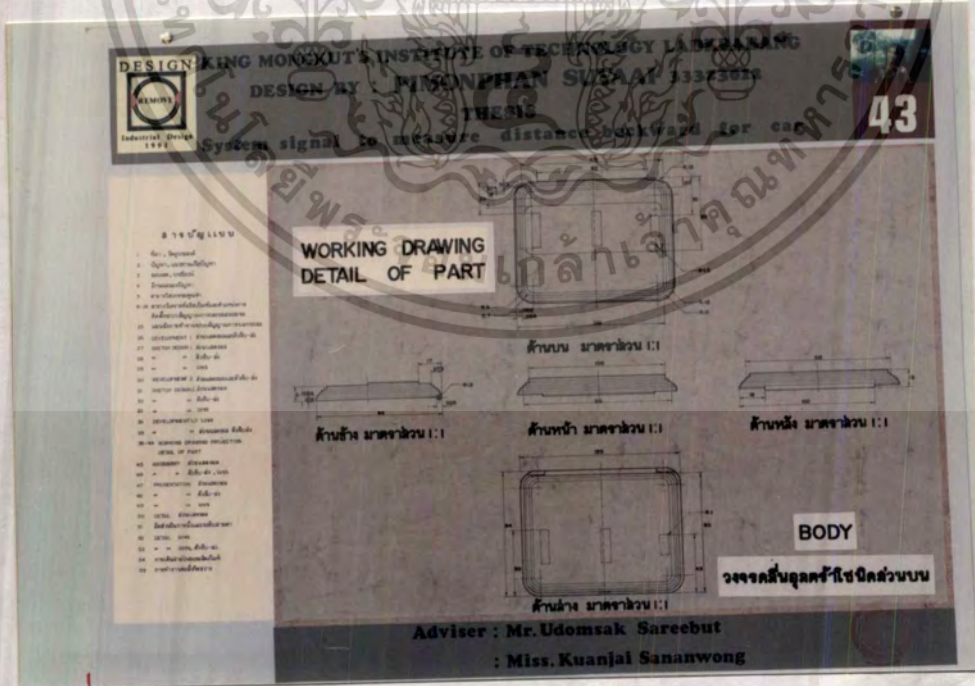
WORKING DRAWING / DETAIL OF PART
